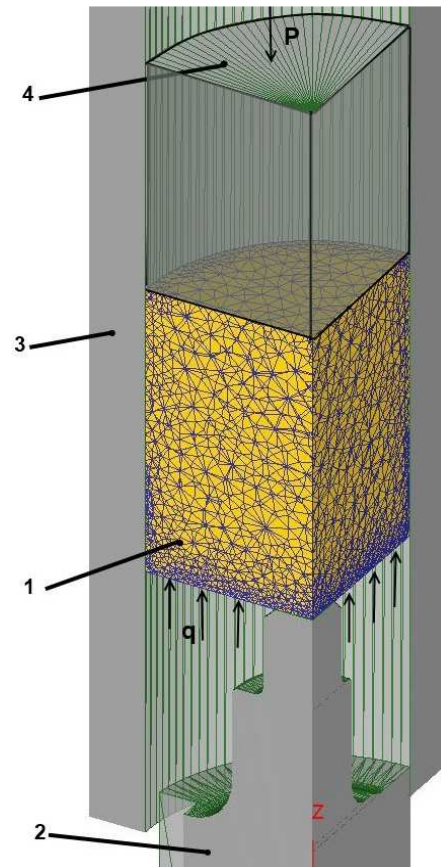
Розрахункова схема видавлювання порожнини пресформи в умовах дії протитиску на позаконтактну поверхню заготовки.
